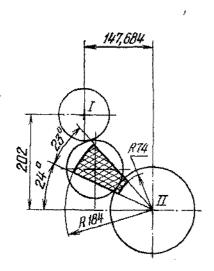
Чертеж для проверки возможности сцепления сменстанках ных шестерен на 16K20, 16K20II, 16K20F
